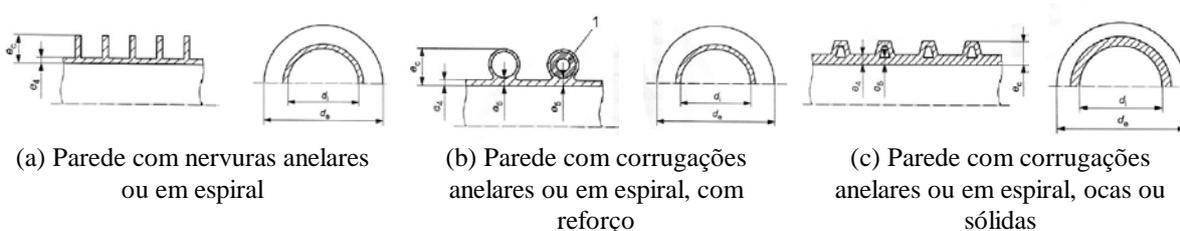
Exemplos típicos de construção de parede do Tipo B (Fonte: ABNT NBR ISO 21138-3:2016).
